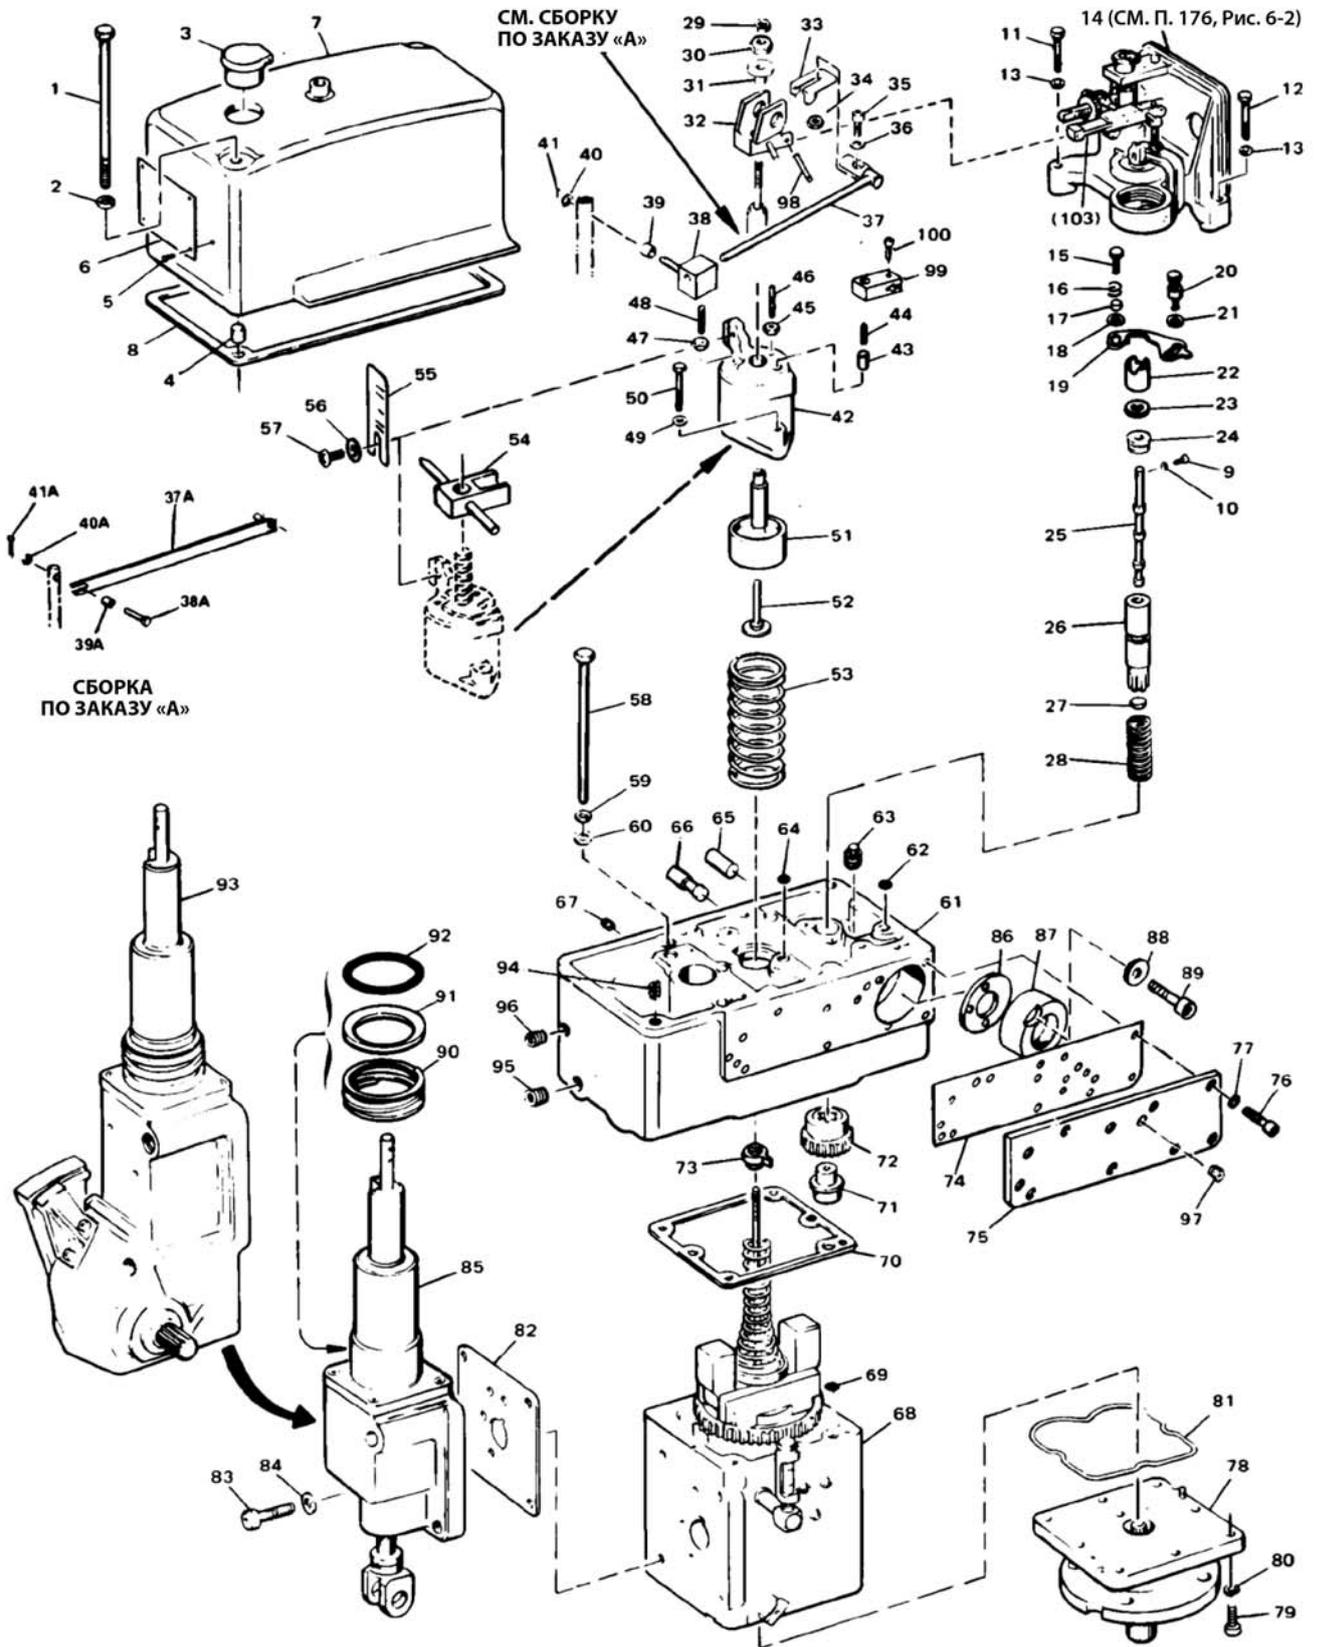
Покомпонентный чертеж длинной колонки PGA
